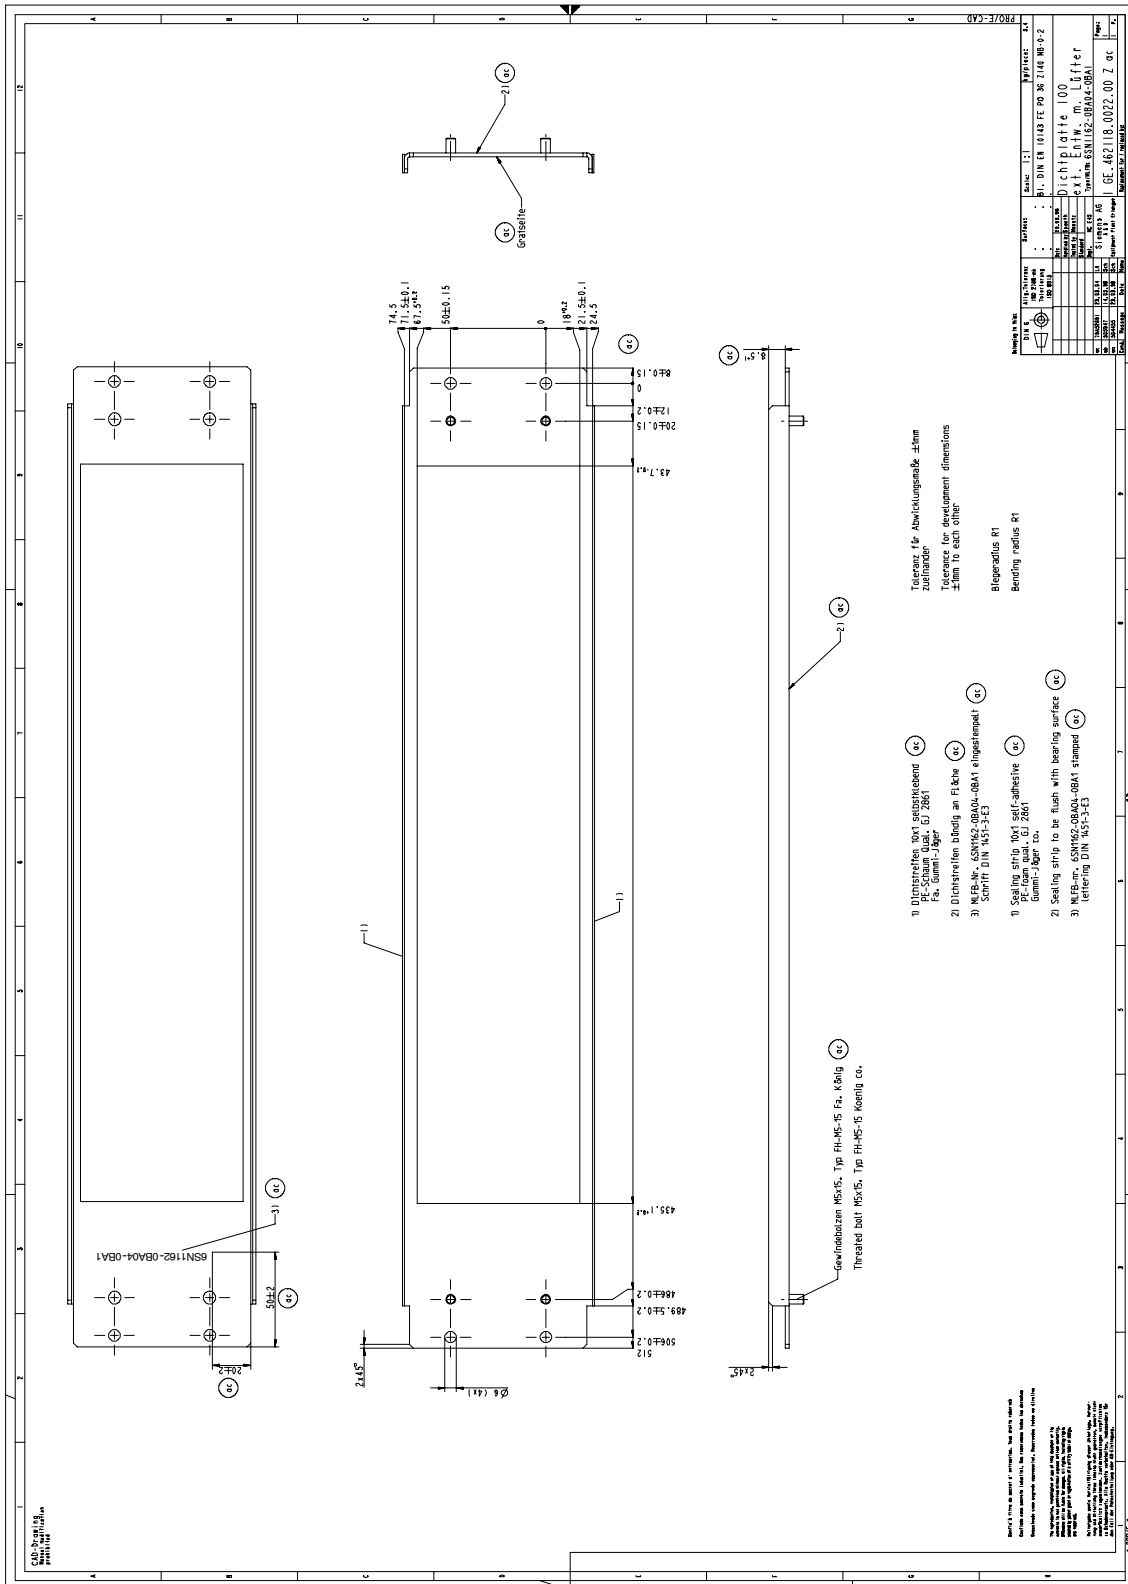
Refroidissement externe, châssis de montage pour le montage d'armoire Largeur de module 100 mm, 6SN1162-OBA04-OBA1
